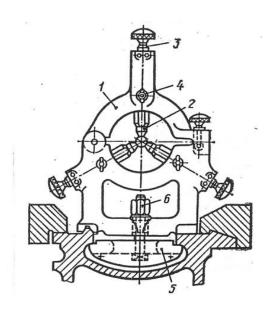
Неподвижный люнет: 1 – откидная крышка; 2 – кулачки; 3 – установочные винты; 4 – болт; 5 – планка; 6 – гайка
